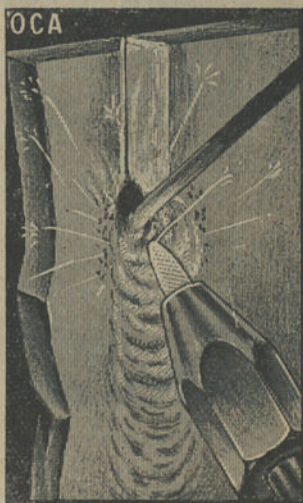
Execução de uma soldadura vertical em chapa de 10 m/m (t. n.).
